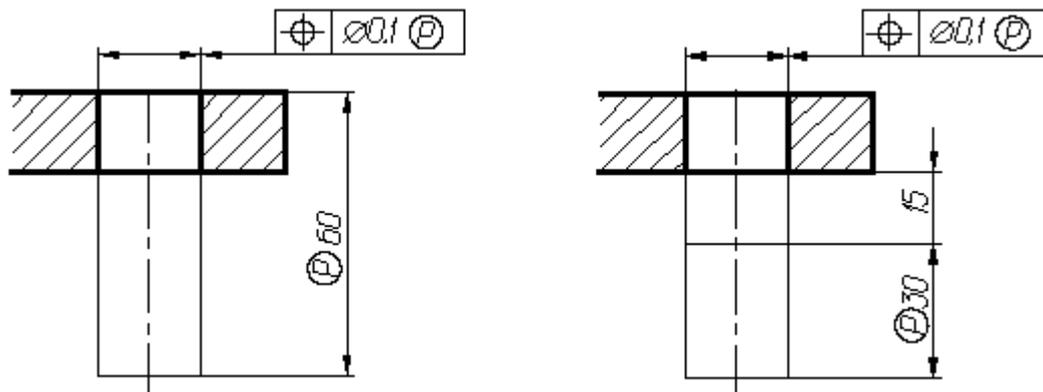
Пример обозначения выступающего поля допуска
